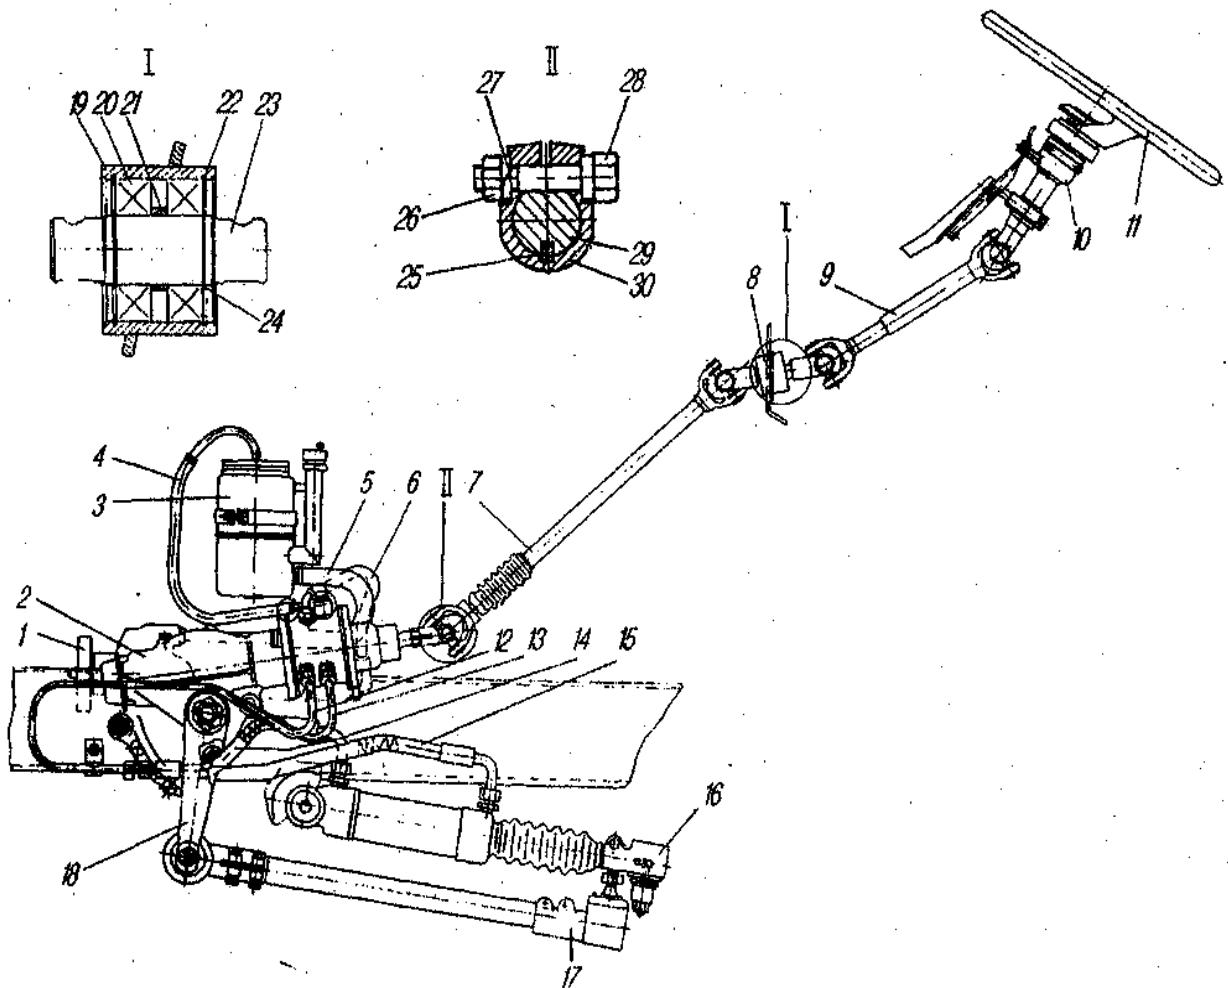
Рулевое управление с механизмом типа червяк-боковой сектор: 1- насос; 2- механизм рулевой; 3-бак масляный; 4,5-шланги низкого давления; 6,14,15-шланги высокого давления; 7,9-валы карданные рулевого управления; 8-опора промежуточная; 10-колонка рулевая; 11-колесо рулевое; 12,13-трубки высокого давления; 16-механизм усилительный; 17-тяга сошки; 18-сошка; 19-корпус; 20-подшипники; 21-втулка распорная; 22,24-кольца стопорные; 23-вал; 25-шпонка; 26-гайка; 27-шайба; 28-болт; 29-вал; 30-вилка карданная
